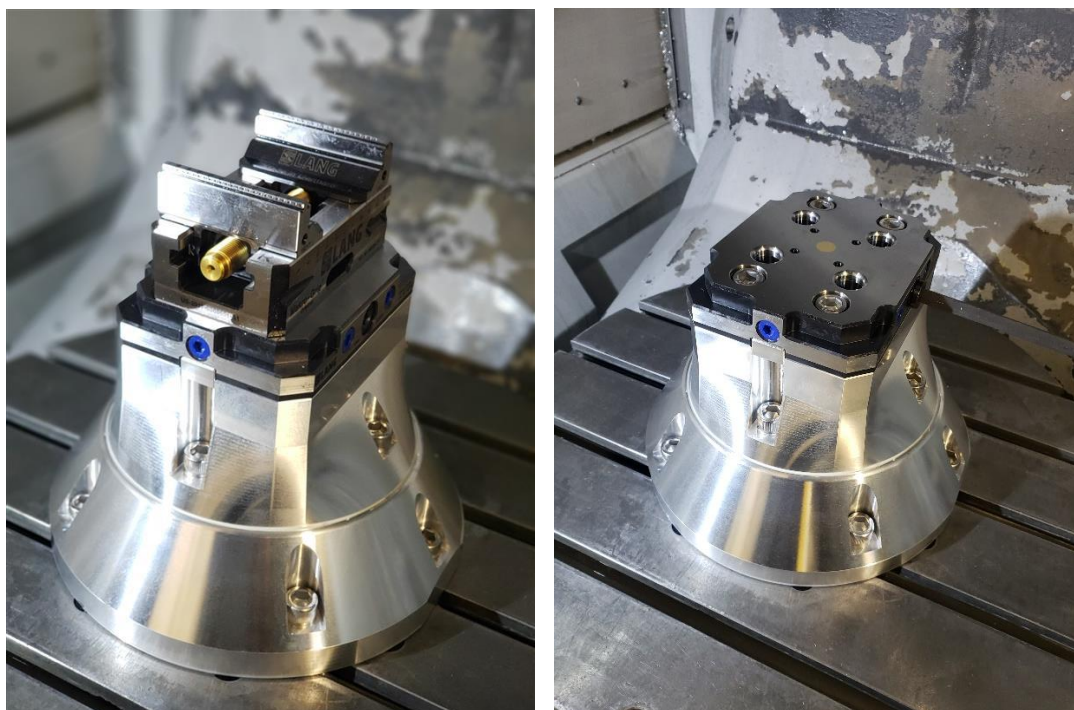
Morsa alto-centrante acoplado com sistema de fixação “zero point”
